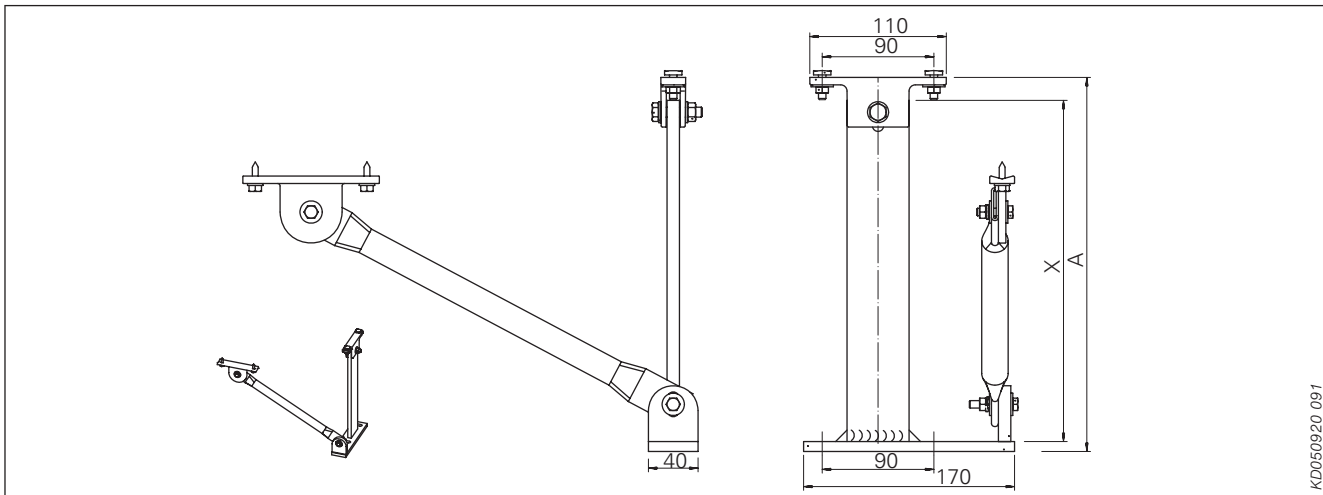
Soporte del carril guía nº 101 (soldado)
